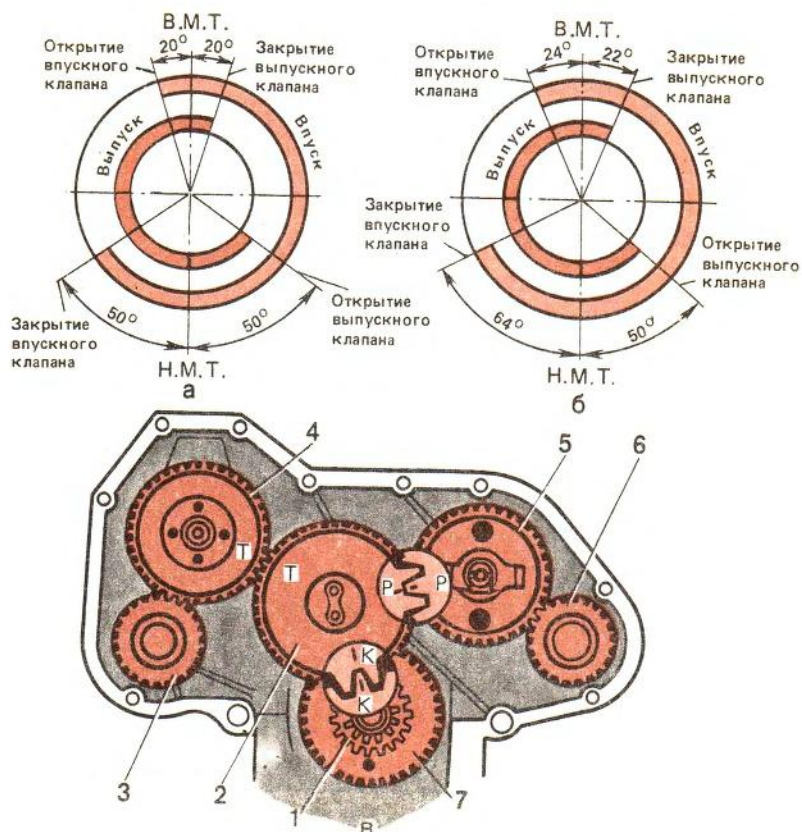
Диаграмма газораспределения и схема расположения зубчатых колес различных механизмов двигателя:
